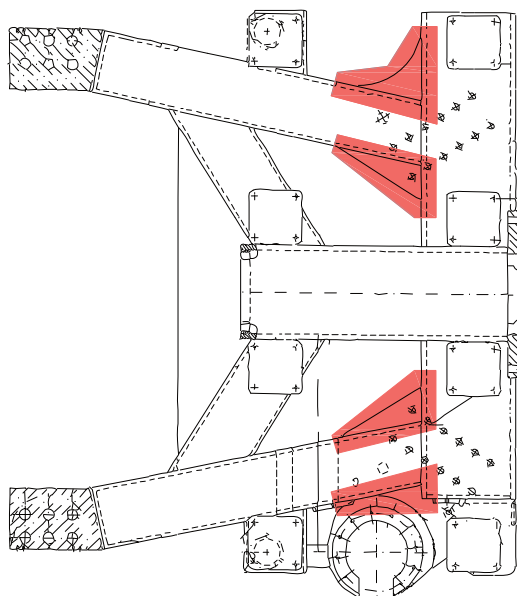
Bastidor trasero del ECO 44/640, resaltándose la zona reforzándose mediante soldadura.
